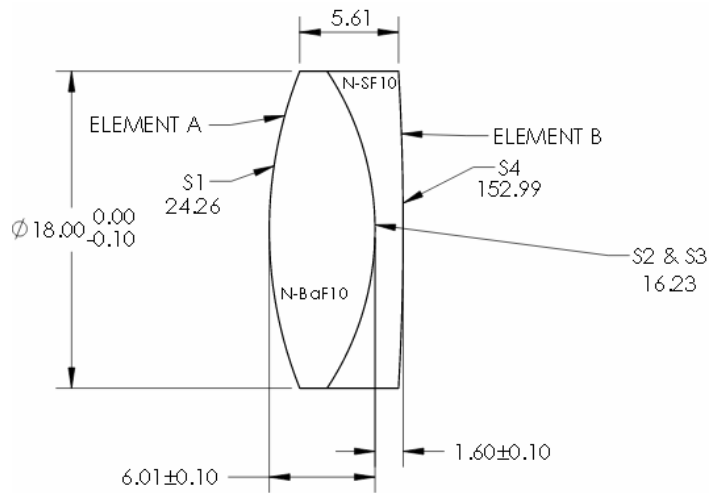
Чертеж ахроматической линзы Edmund #47-706.
